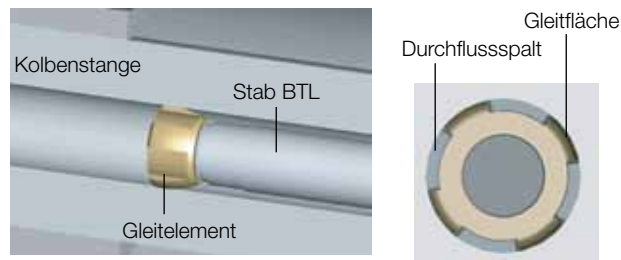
Detailsicht und Draufsicht Gleitelement
